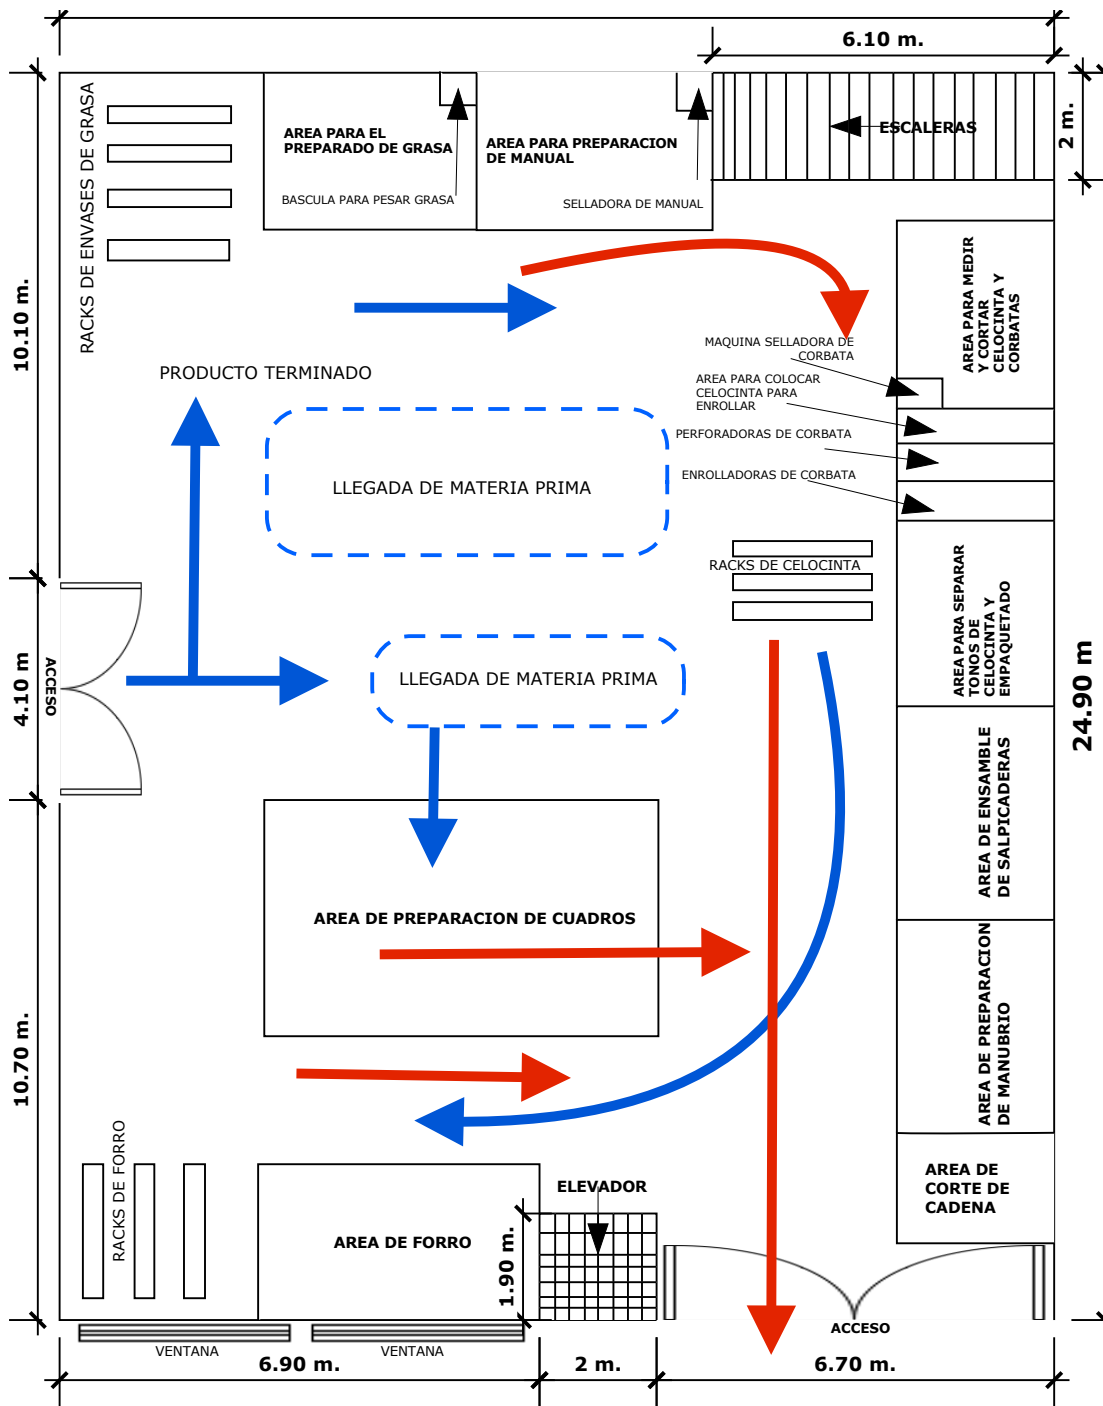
Nuevo Layout de la planta Benotto "Área de pre-ensambles"
